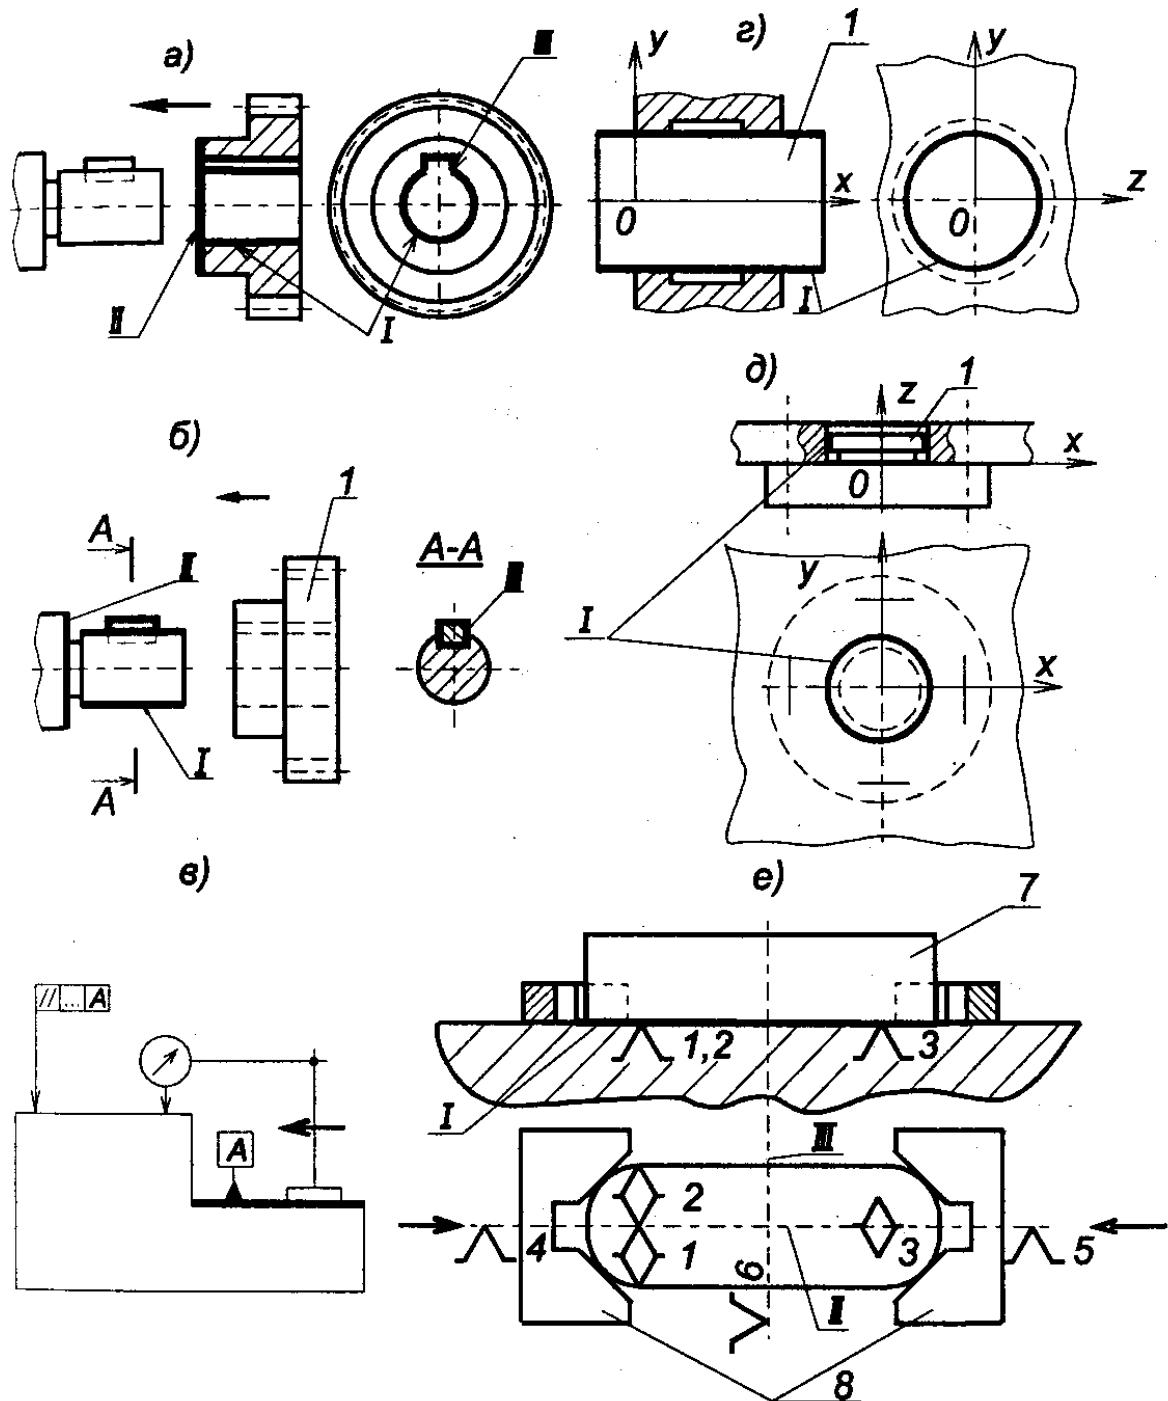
Виды баз: а – основные базы шестерни (I, II, III); б – вспомогательные базы вала (I, II, III) с присоединяемой деталью (1); в – измерительная база (A); г – двойная направляющая база (I) детали (1); д – двойная опорная база (I) детали (1); е – установочная явная база (I) заготовки (7), направляющая скрытая база (II), опорная скрытая база (III), 1...6 – опорные точки, 8 – губки самоцентрирующих тисков
